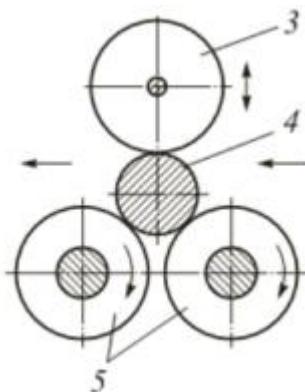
Сечение для поперечной правки изгибом на роликах при обкатке с прижатием заготовки
